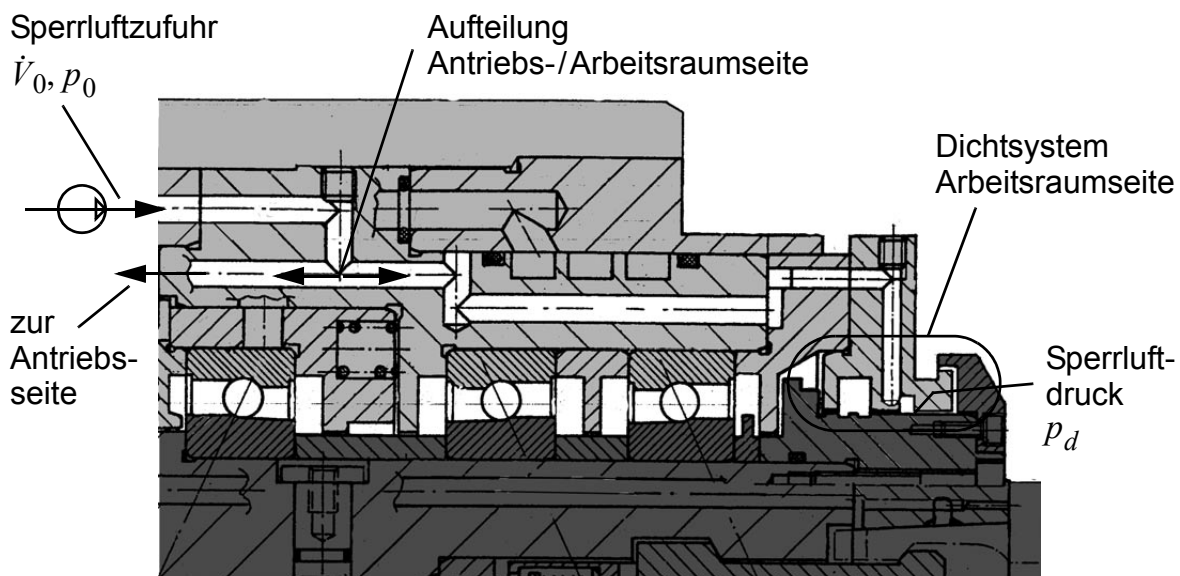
Ausführungsbeispiel der Sperrluftzuführung in einer Frässpindel $\varnothing 70$ mm, Werkzeugaufnahme HSK63
